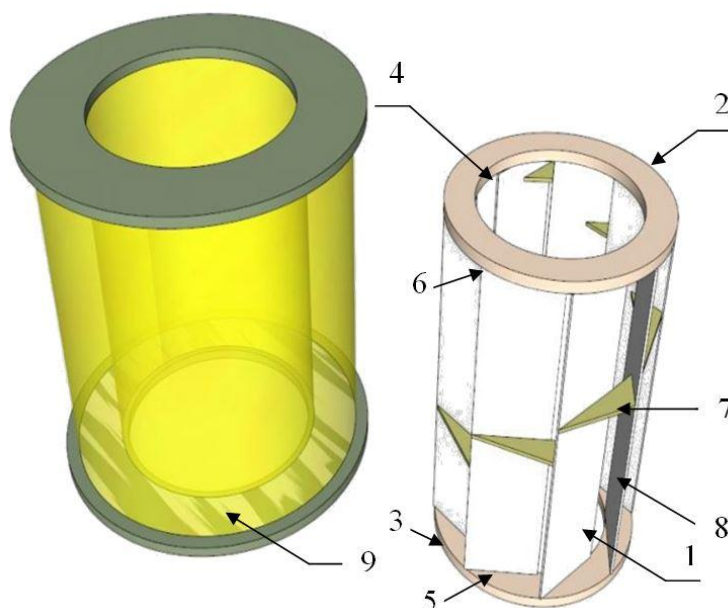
Общий вид устройства воздухоподготовки
